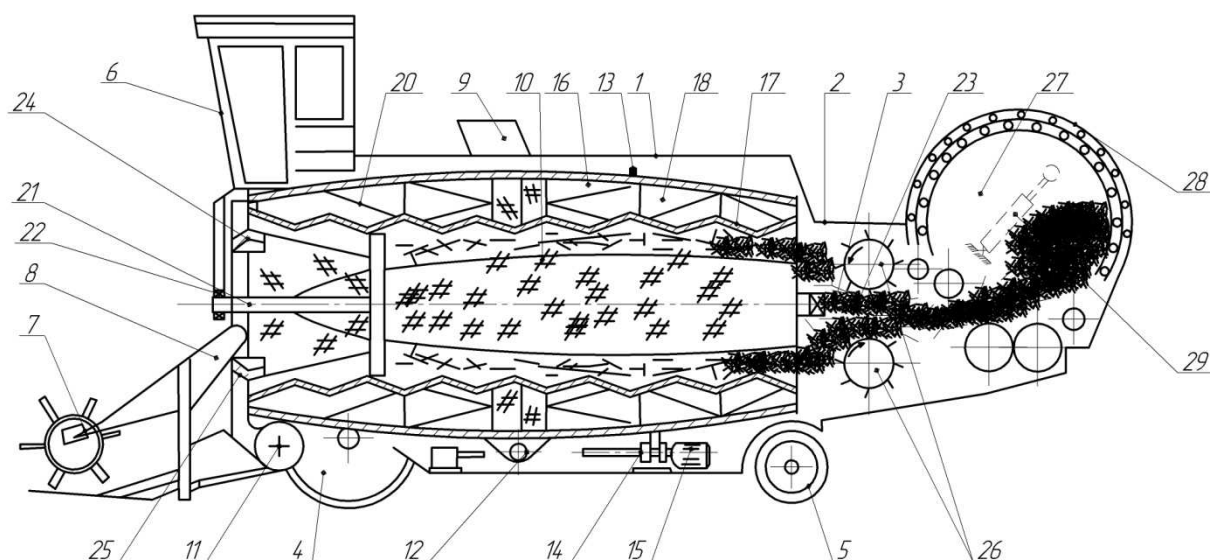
Технологическая схема прямоточного зерноуборочного комбайна
